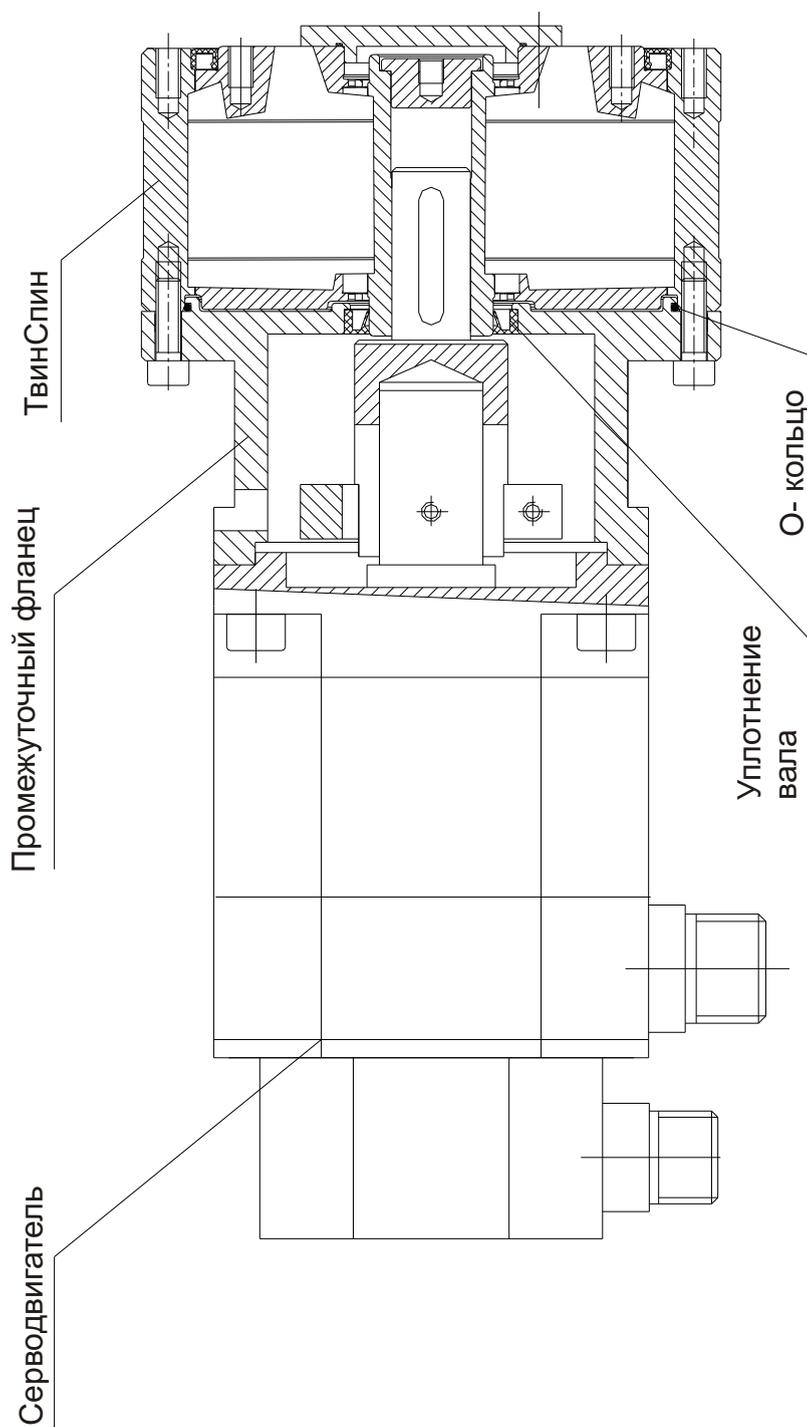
Typical installation example / ТГПримеры возможной установки
